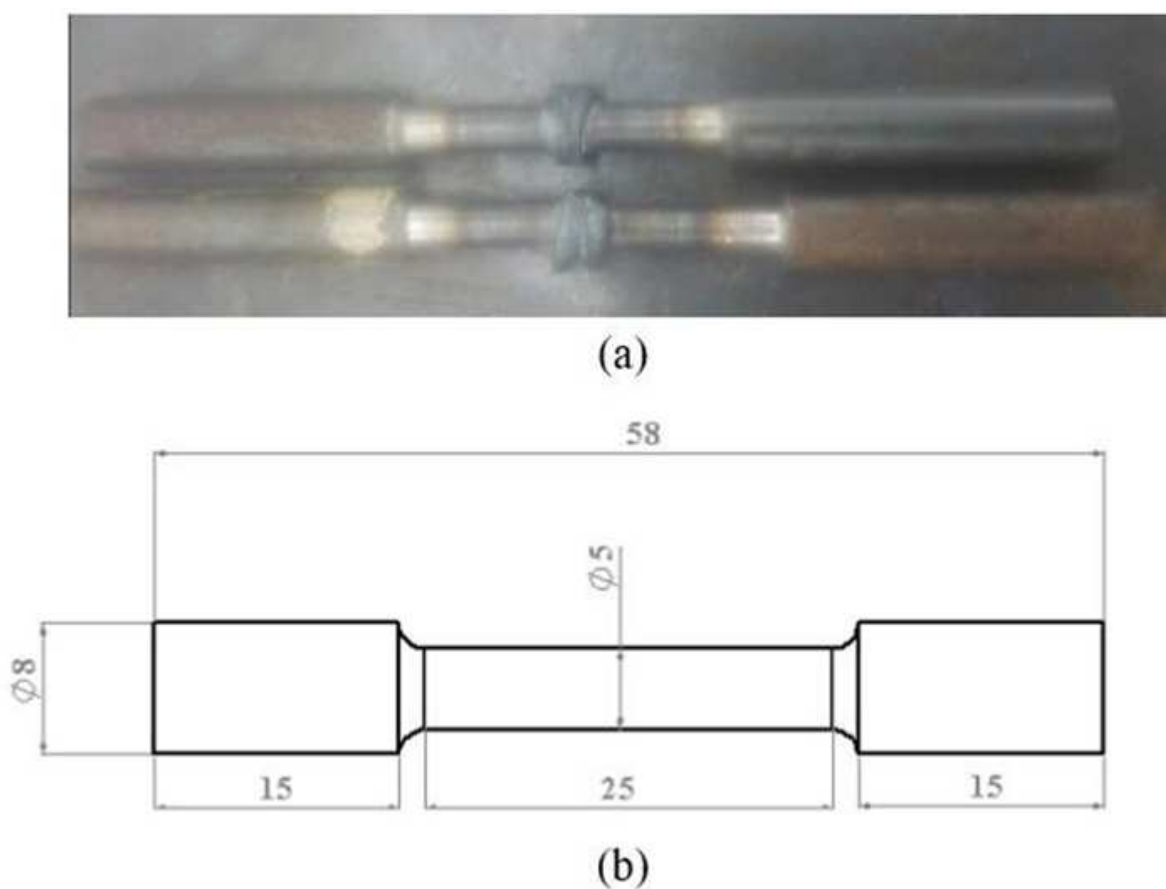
Corpos de prova para o ensaio de tração. (a) corpos de prova do ensaio de solda por fricção. (b) desenho do corpo de prova do ensaio de tração com dimensões em milímetros.
